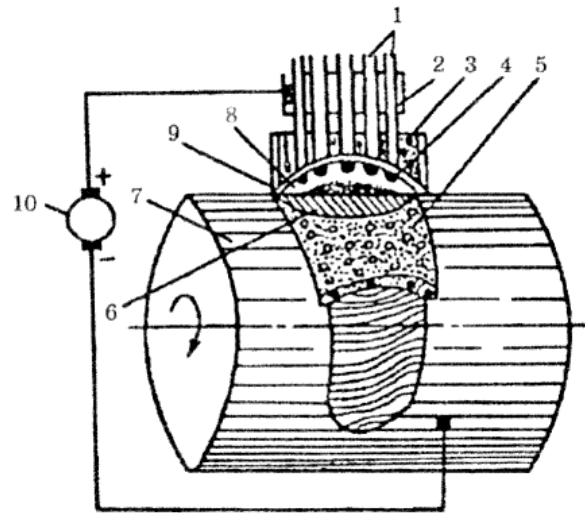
Багатоелектродне наплавлення під шаром флюсу: 1 – електроди; 2 – струмопідвідний контакт; 3 – флюс; 4 – електрична дуга; 5 – шлакова кірка; 6 – наплавлений метал; 7 – відновлювана деталь; 8 – газова бульбашка; 9 – оболонка розплавленого флюсу; 10 – джерело струму
